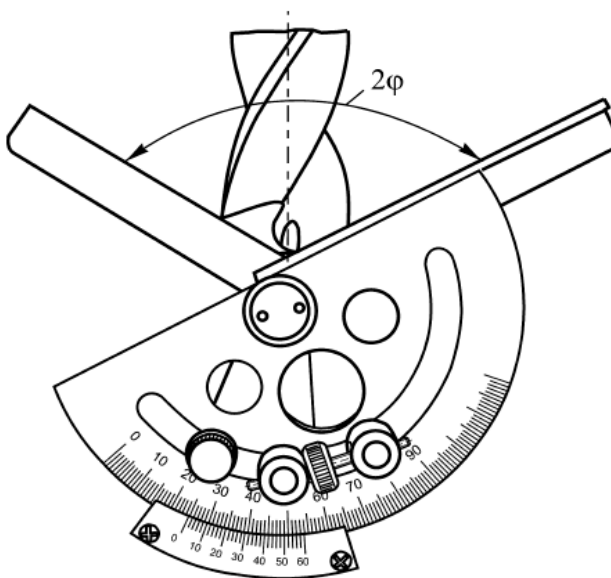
Схема измерения угла 2φ при вершине сверла
